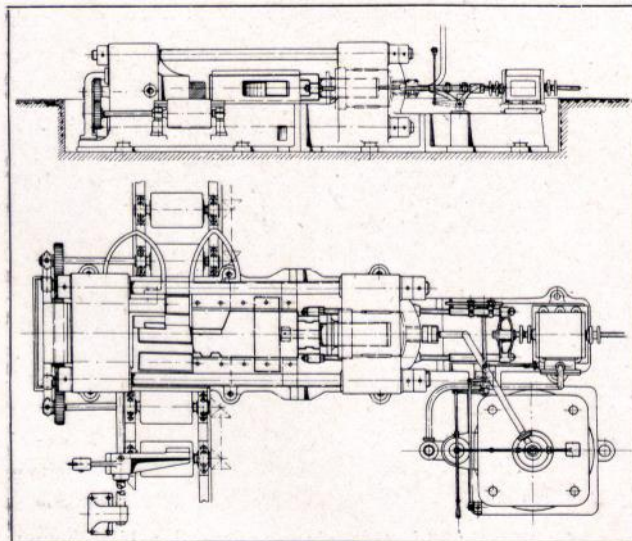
Horizontale Blockschere mit hydraulischem Antrieb.
